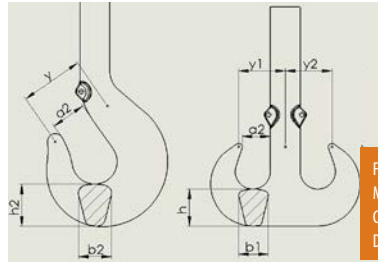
MEDIDAS DE CONTROLE DIMENSIONAL
